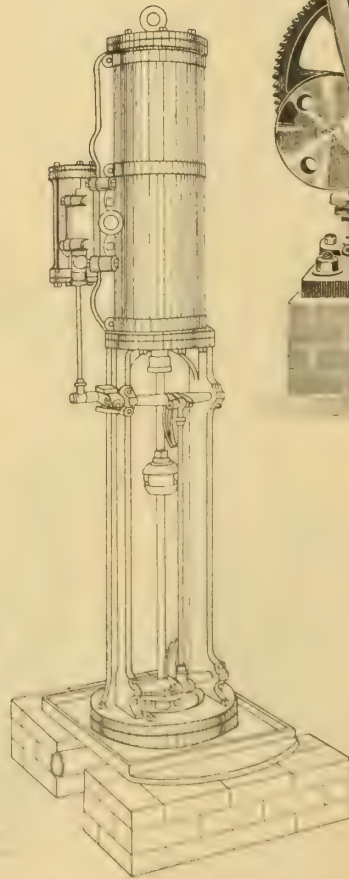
Dampfmaschine für den Antrieb von Bohrlochpumpen.
